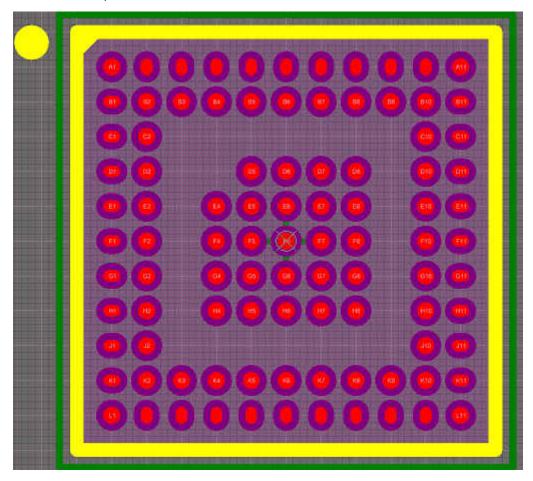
Top View Alternate TPS65982 Footprint (Oval Pads)
